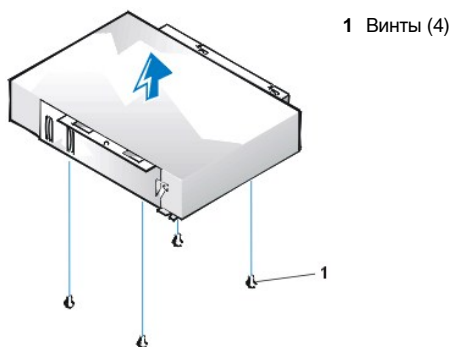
Извлечение 3,5-дюймового дисководов гибких дисков с креплением
